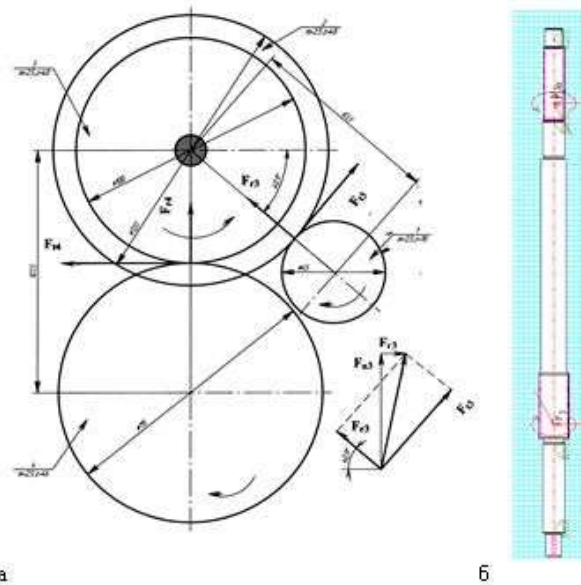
Розгортка приводу верстата: а – схема розгортки; б – розрахункова схема вала
